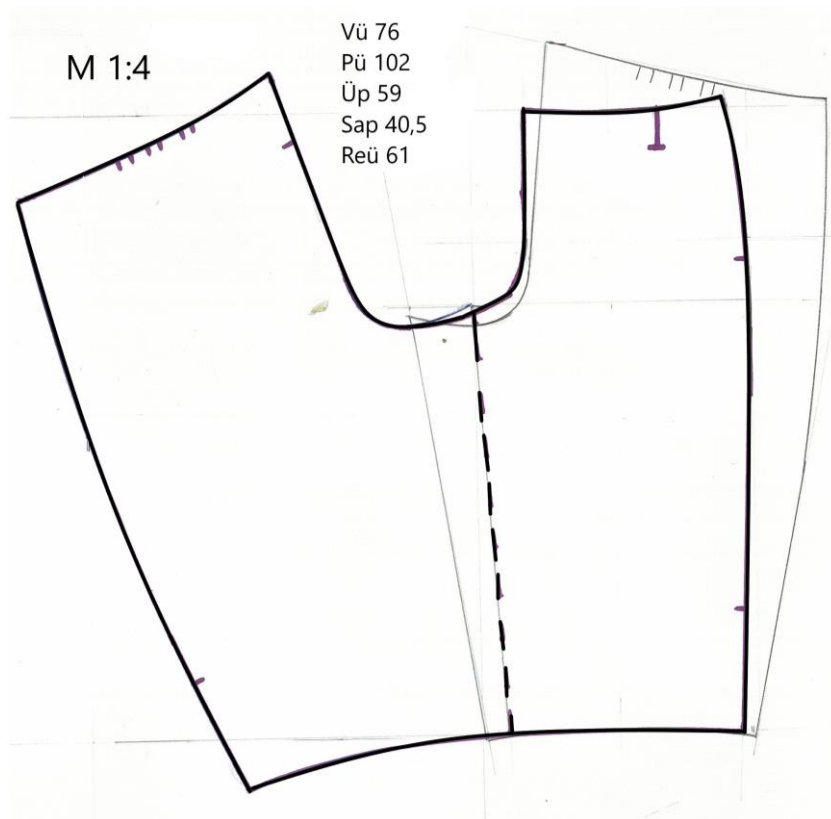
Konstruksioonijoonete nimetused. (Allikas: Paju, 2017, lk13)
